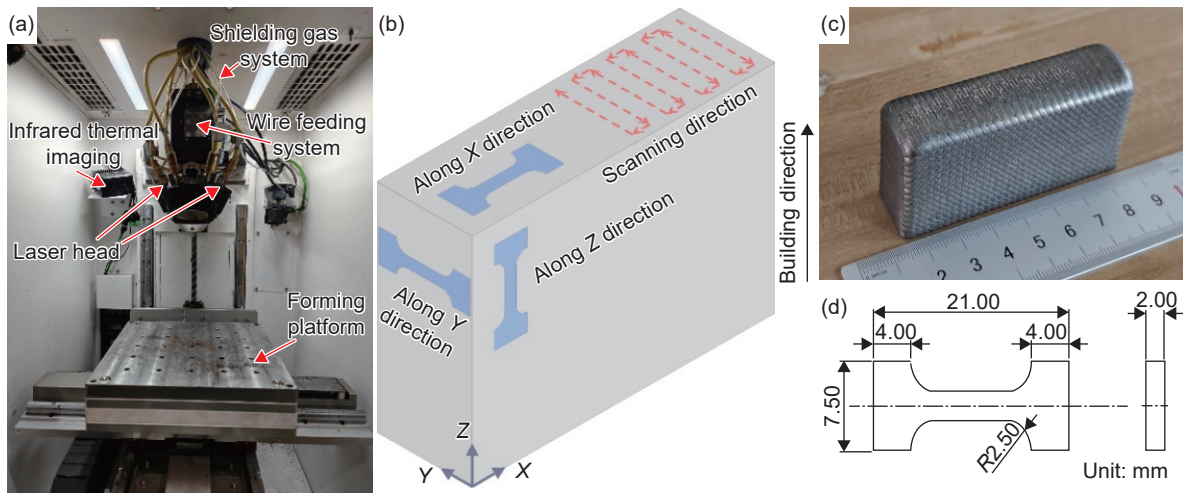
W-LDED 成形设备及试样 (a)W-LDED 成形系统; (b)拉伸试样取样示意图; (c)成形合金块实物图; (d)拉伸试样尺寸示意图;
